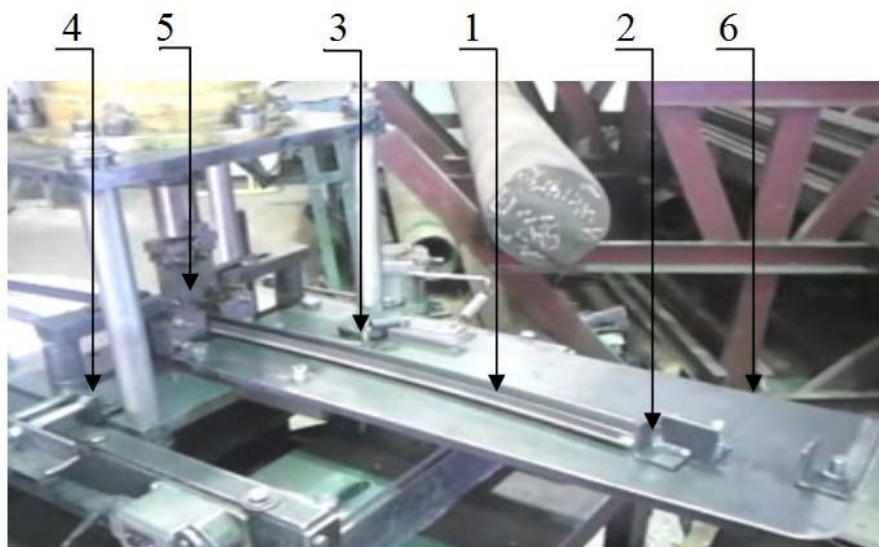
Пресс пневматический: 1- профиль, 2- упор, 3- сбрасывающий механизм, 4- каретка, 5- штамп отрубной, 6- платформа.
